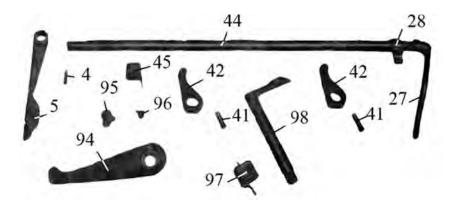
Детали механизма повторного взведения: 4- штифт; 5- рычаг; 27- ручка; 28- клипс; 41- стопор; 42- кулачок; 44- ось; 45- пружина; 94- рычаг; 95, 96- винт; 97- пружина повторного взвода; 98- ось повторного взвода
